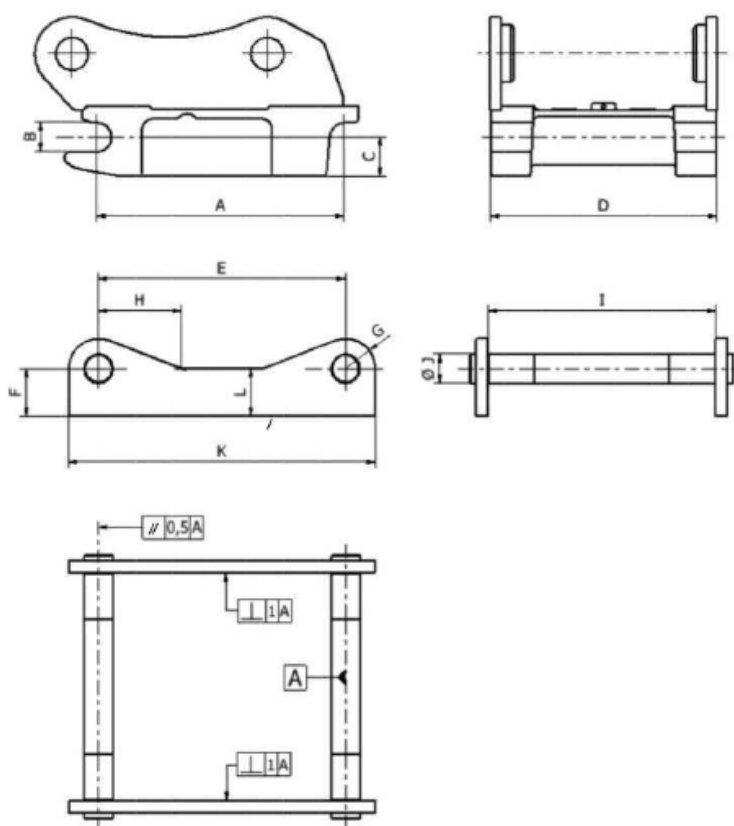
Eliminace tolerancí v zadním upínacím čepu
